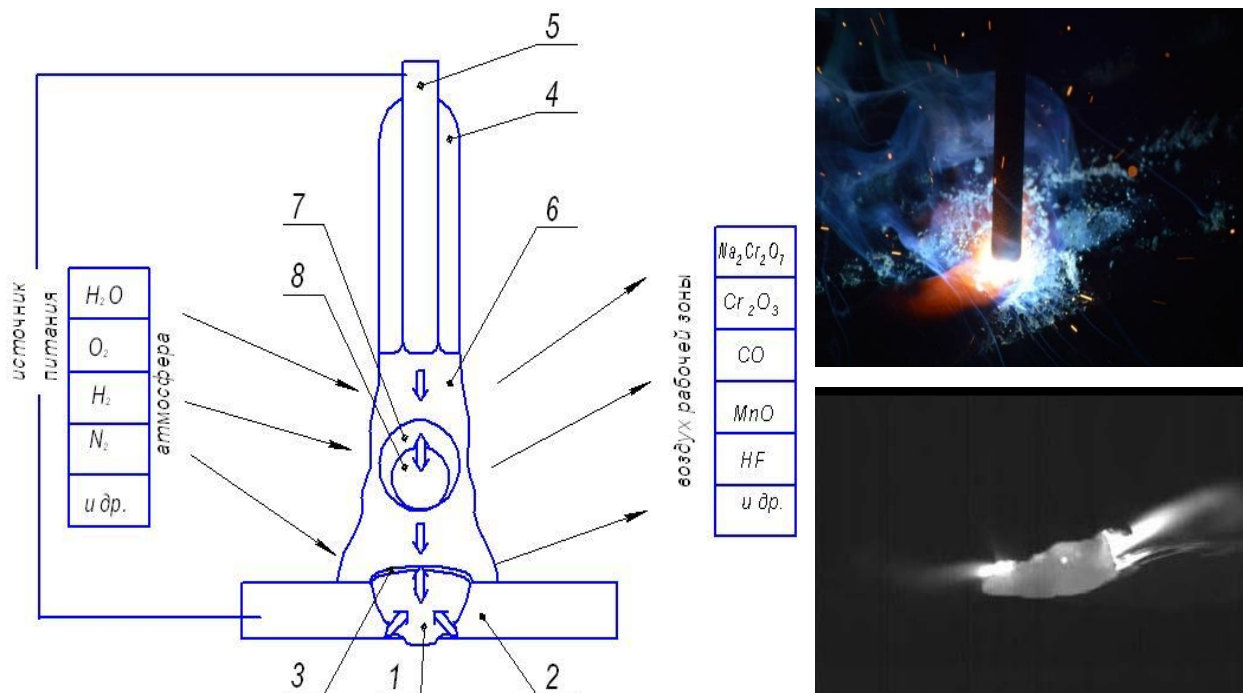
Физическая модель процесса РДС: 1 – наплавленный металл; 2 – основной металл; 3 – шлаковая корка на поверхности сварного шва; 4 – обмазка (покрытие) электрода; 5 – металлический стержень электрода; 6 – газовая атмосфера; 7- шлаковая фаза капли; 8 – металлическая фаза капли
